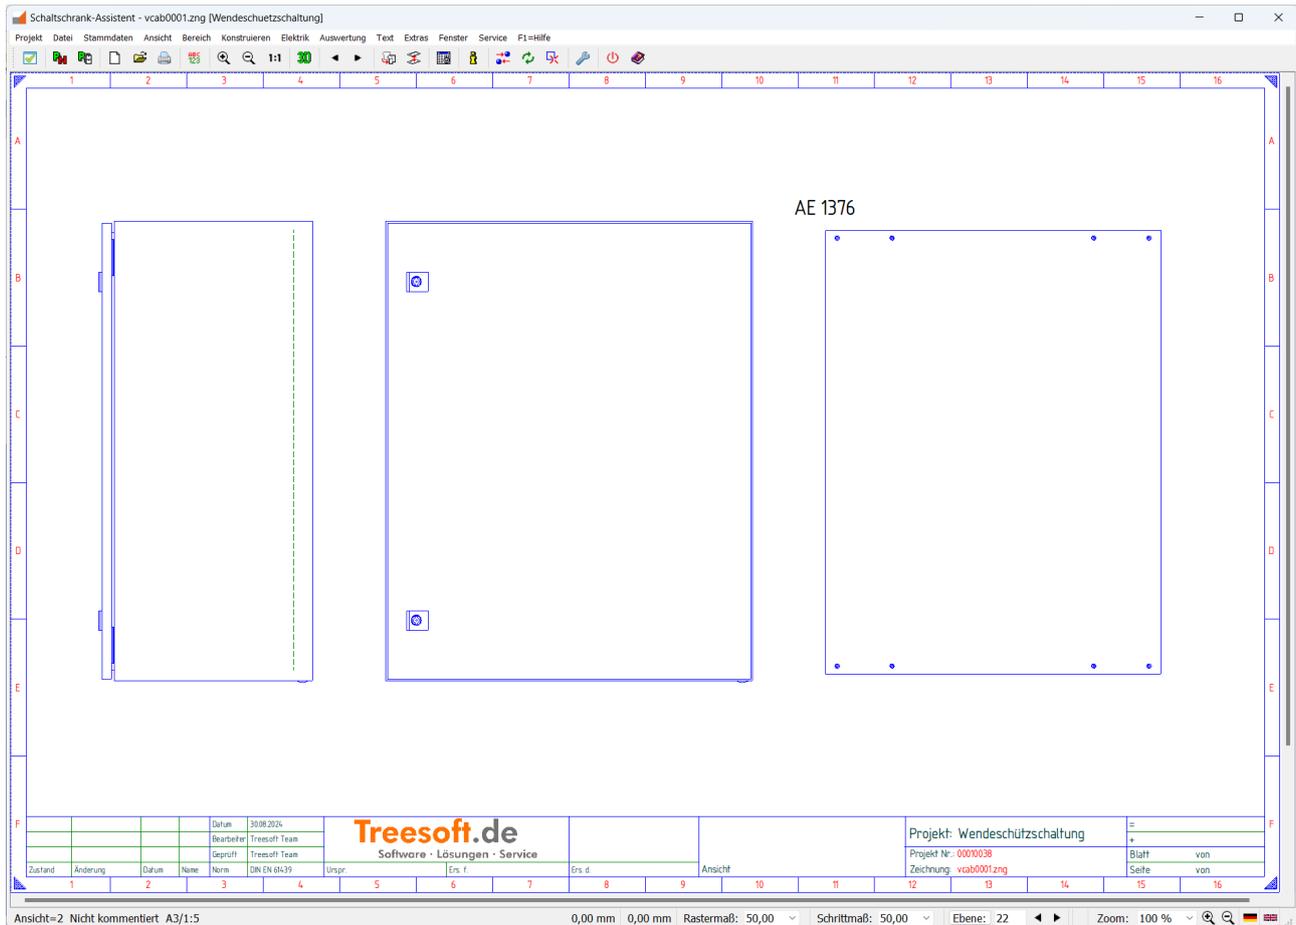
Gewählte Kombinationsvariante des Schaltschranks (Seitenansicht/Frontansicht/Montageplatte)
